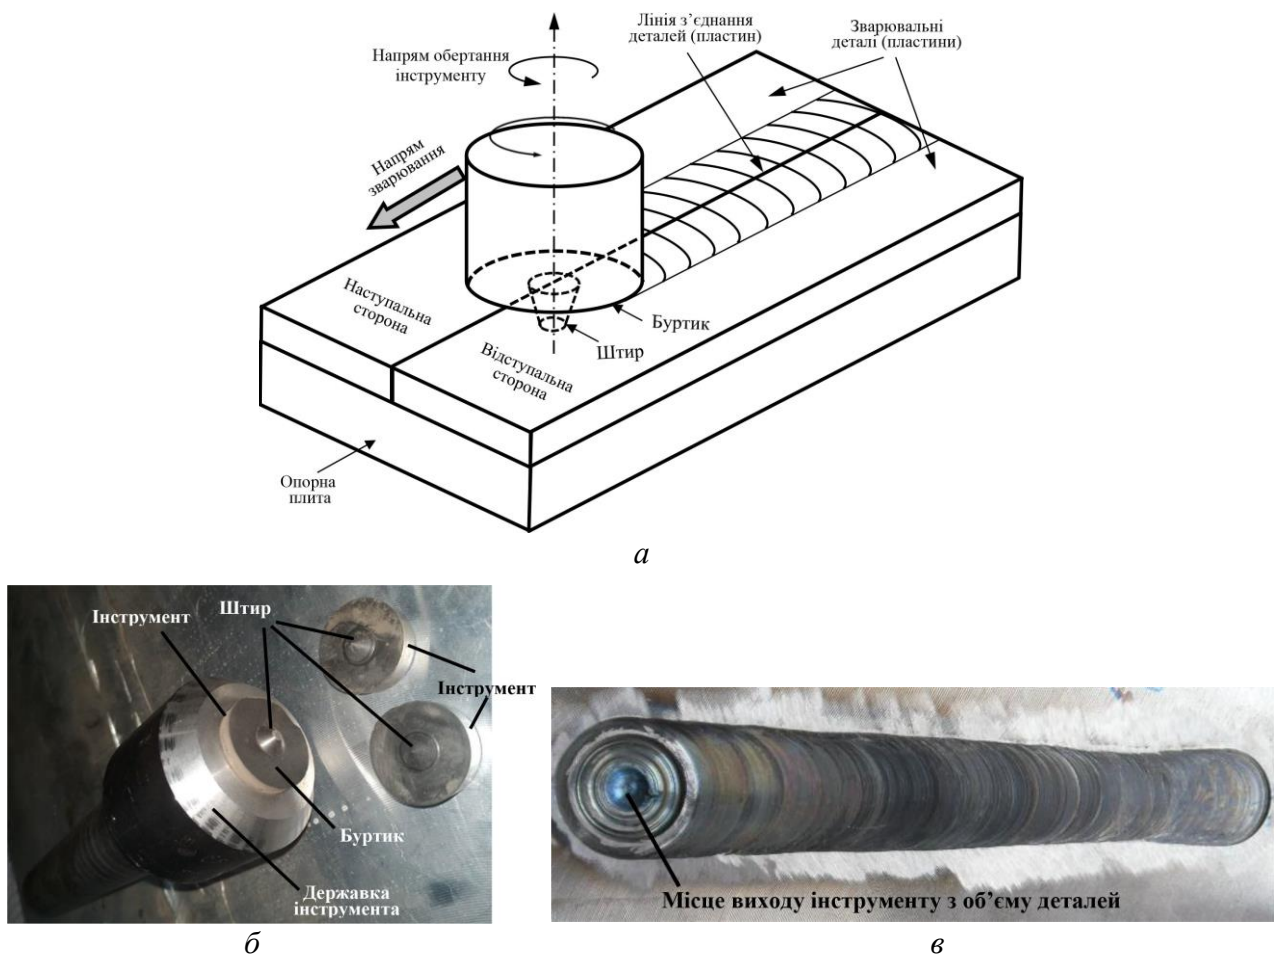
Схематична ілюстрація процесу ЗТП (а); розроблений інструмент із кибориту (б) [6]; вигляд зварного шва в результаті зварювання двох пластин зі сталі AISI 304 (в)
